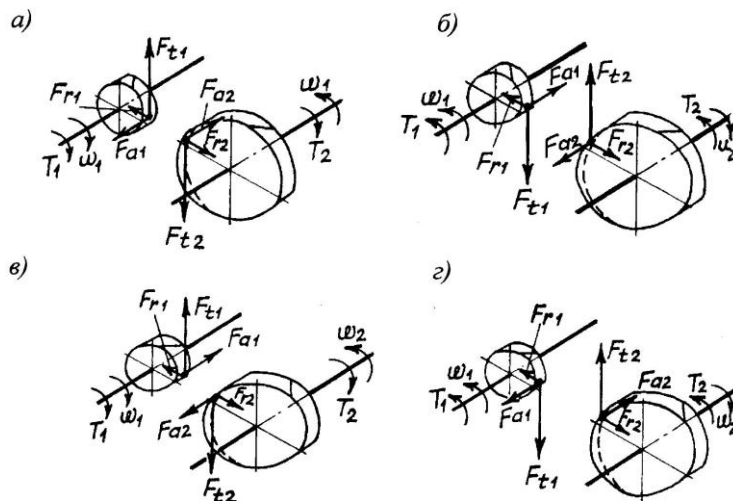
Схема сил в зацеплении косозубой цилиндрической передачи:
